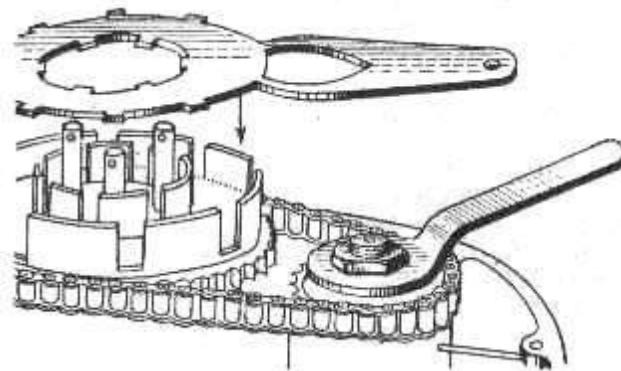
Фиксация звездочки коленчатого вала и барабанов сцепления
